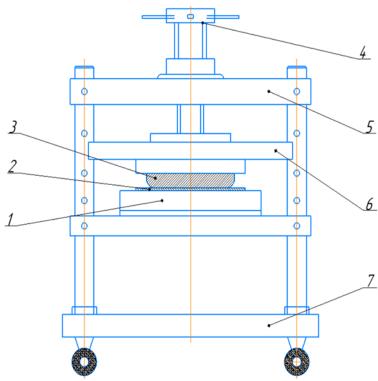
Схема пресса портального типа с механическим приводом: 1 — индуктор; 2 — заготовка; 3 — оснастка; 4 — механизм подъема-опускания; 5 — фиксирующие штыри; 6 — подвижная плита; 7 — основание
